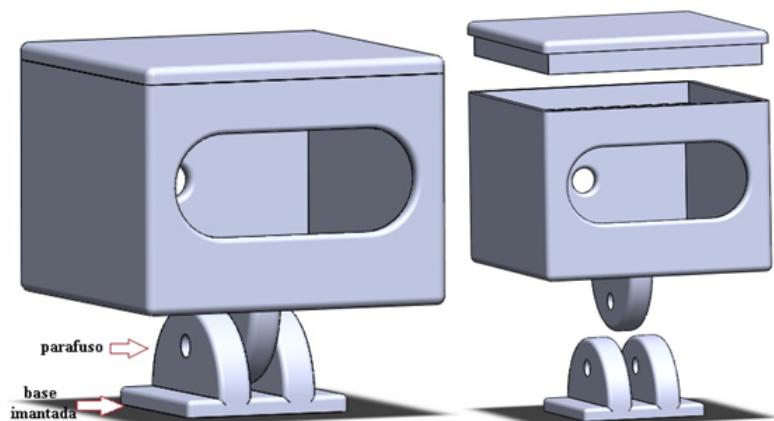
Case para acoplamento do sensor: montado e vista explodida
